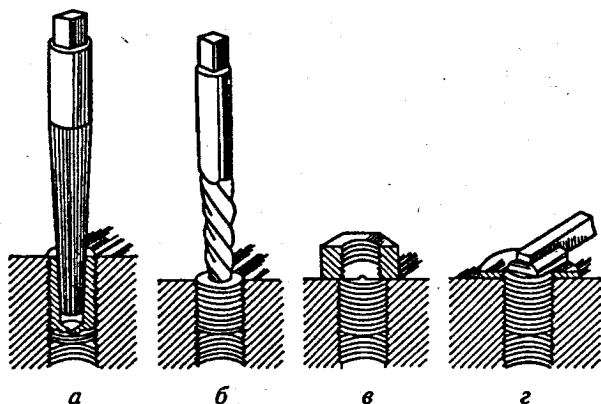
Инструменты и приемы для вывертывания обломанных шпилек:
